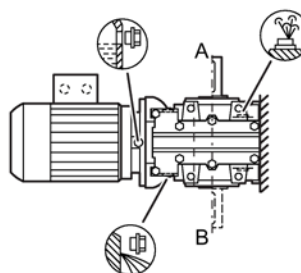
Монтажные положения для цилиндрического косозубого редуктора С. в исполнении на лапах, типоразмер 29
